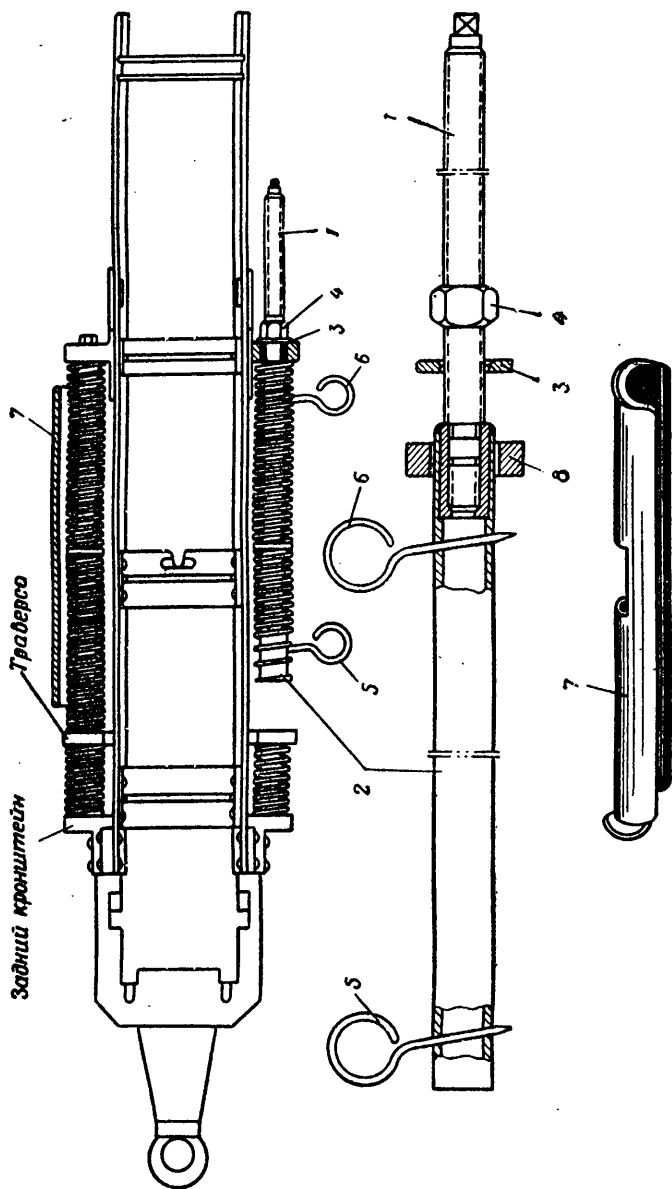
Приспособление для разборки и сборки амортизатора в минометах с отъемными передними кронштейнами:
